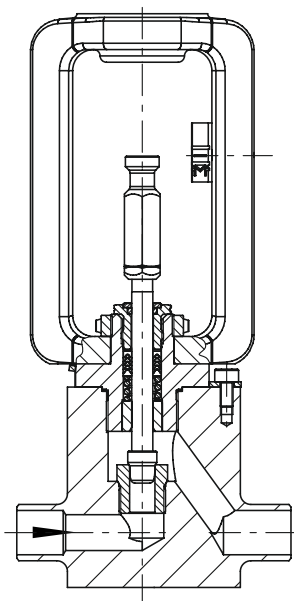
Hochdruckventil Typ 3252 als Durchgangsventil mit Anschweißenden
